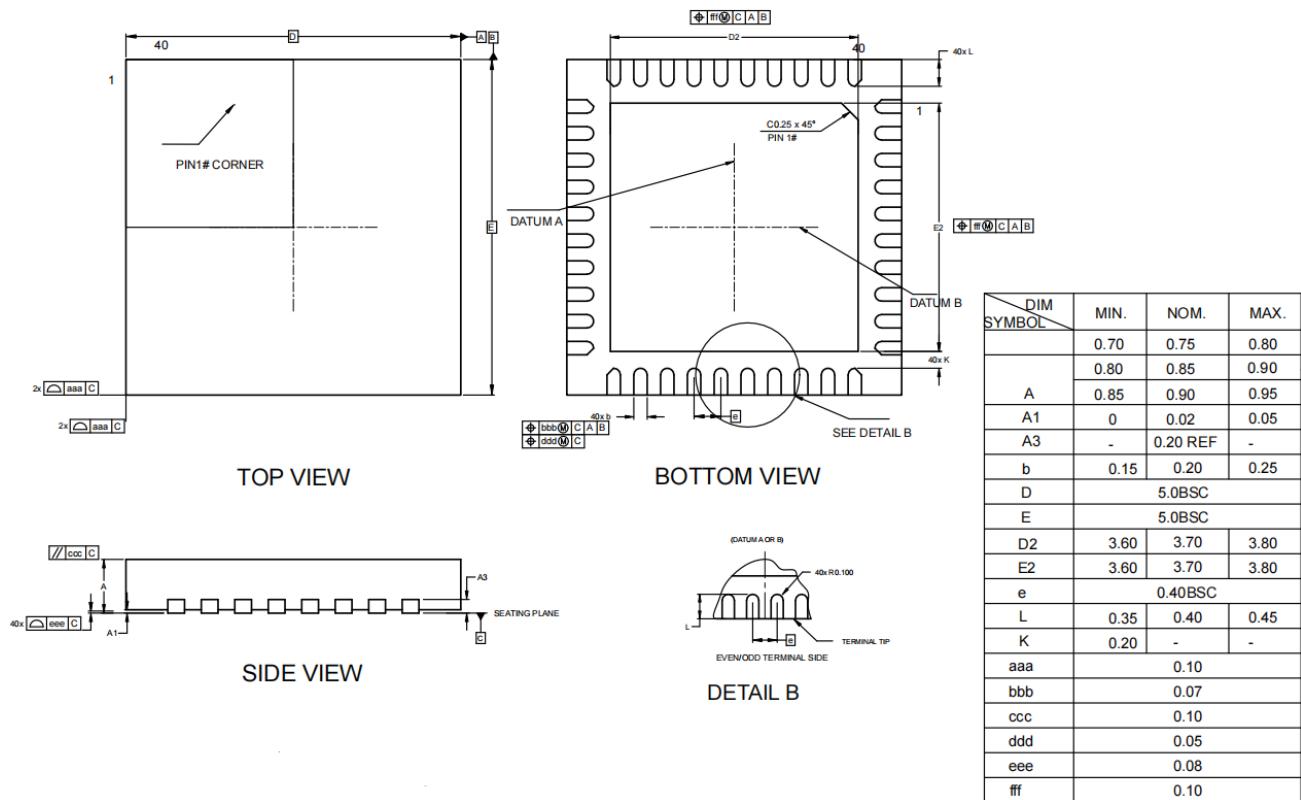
QFN40 (5*5*0.75-P0.4) 封装外形尺寸
